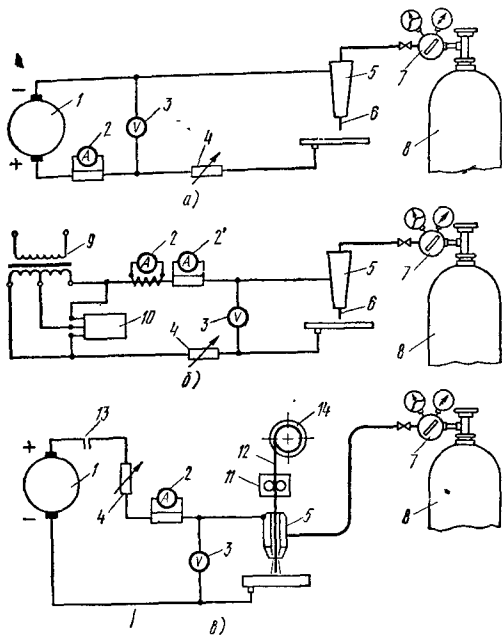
Электрическая и газовая схемы сварки в защитных газах:
